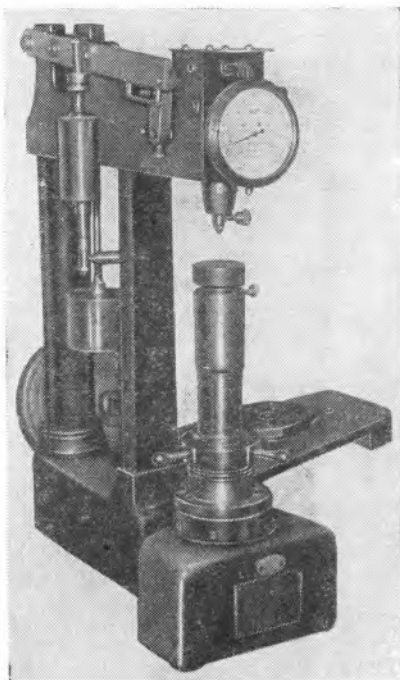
Прибор типа «Роквелл» для определения твердости абразивных инструментов на керамической и бакелитовой связках зернистостью 12 и мельче
